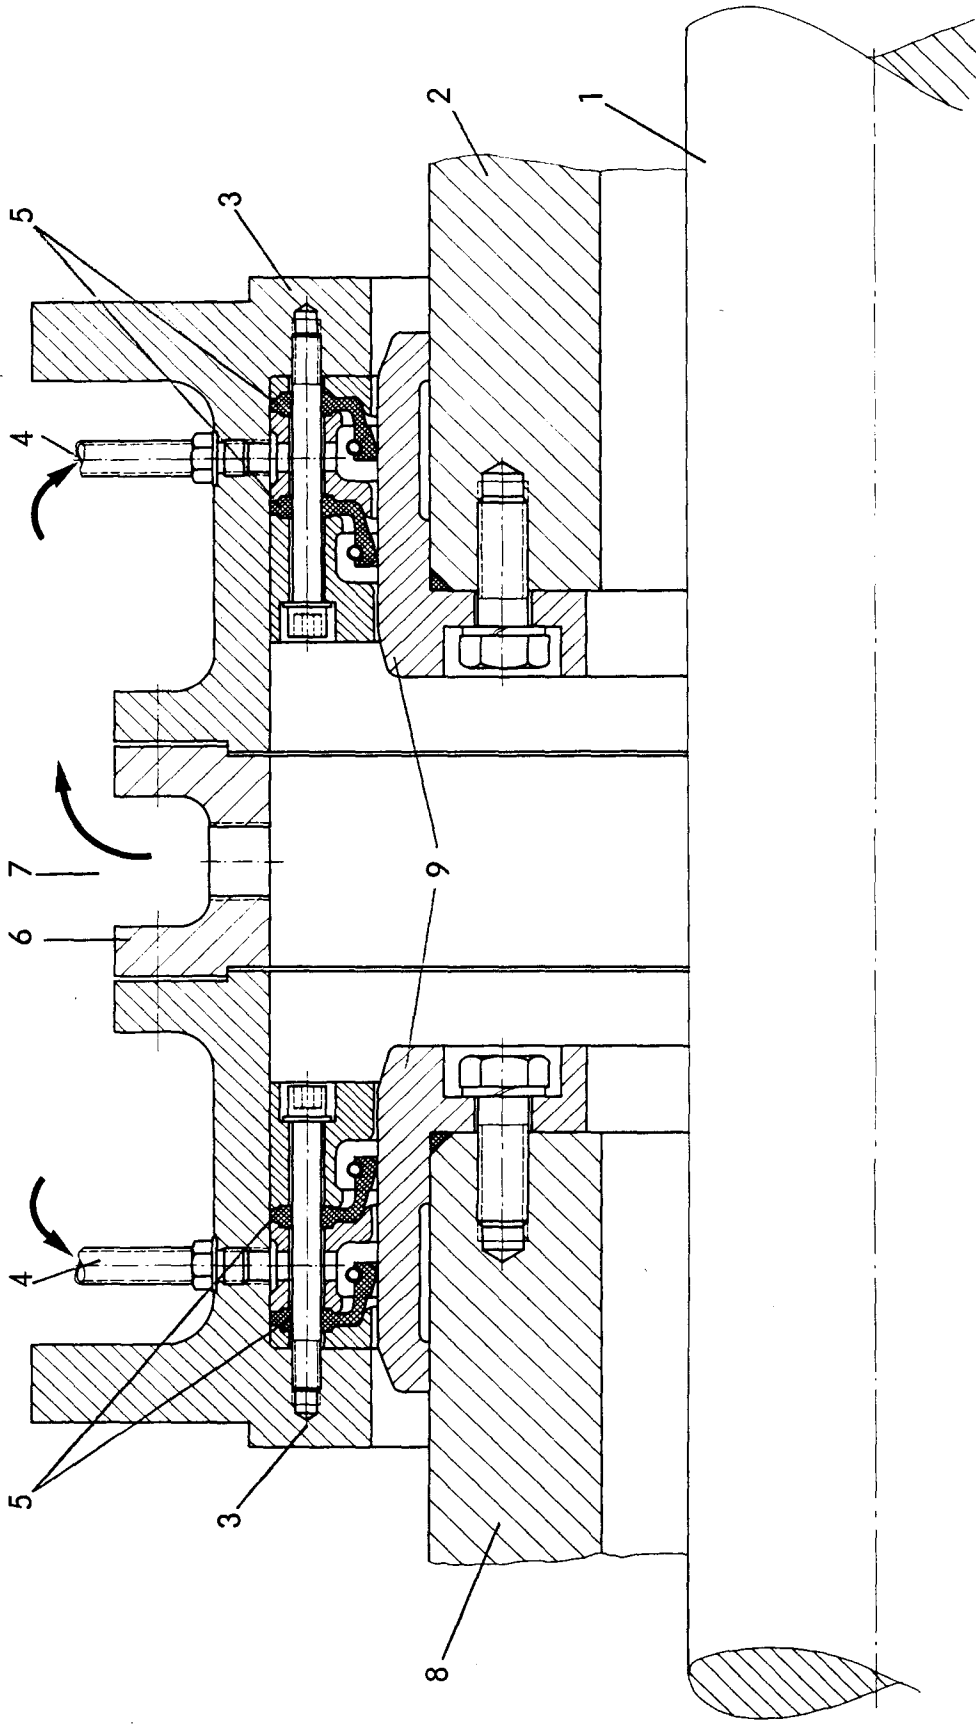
Innenwellen-Innendichtung für den Anbau an die Getriebe
